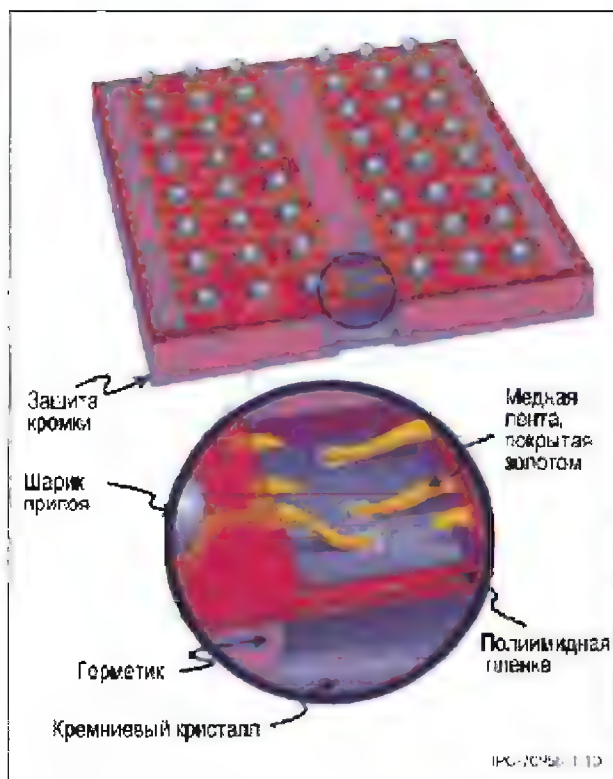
Подложка корпуса  $\mu$ BGA на основе полиимидной пленки с приваренными выводами обеспечивает надежное соединение между контактными площадками кристалла и шариковыми выводами
